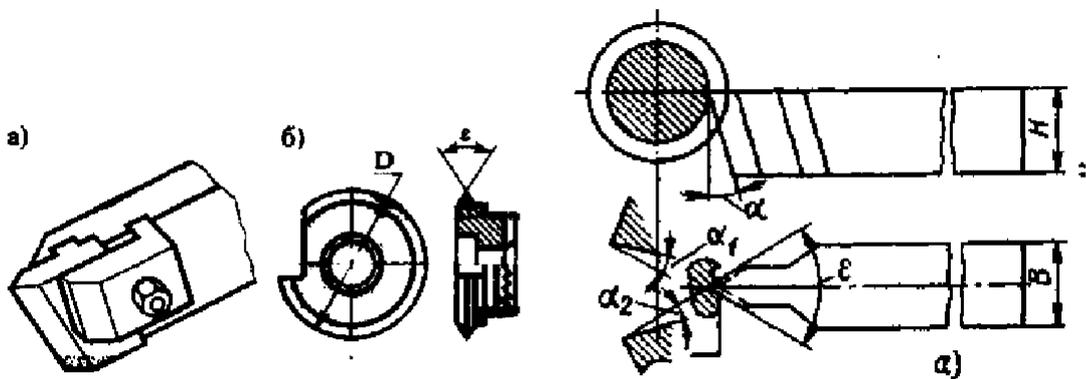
Резьбовые резцы, затачиваемые по передней поверхности:
